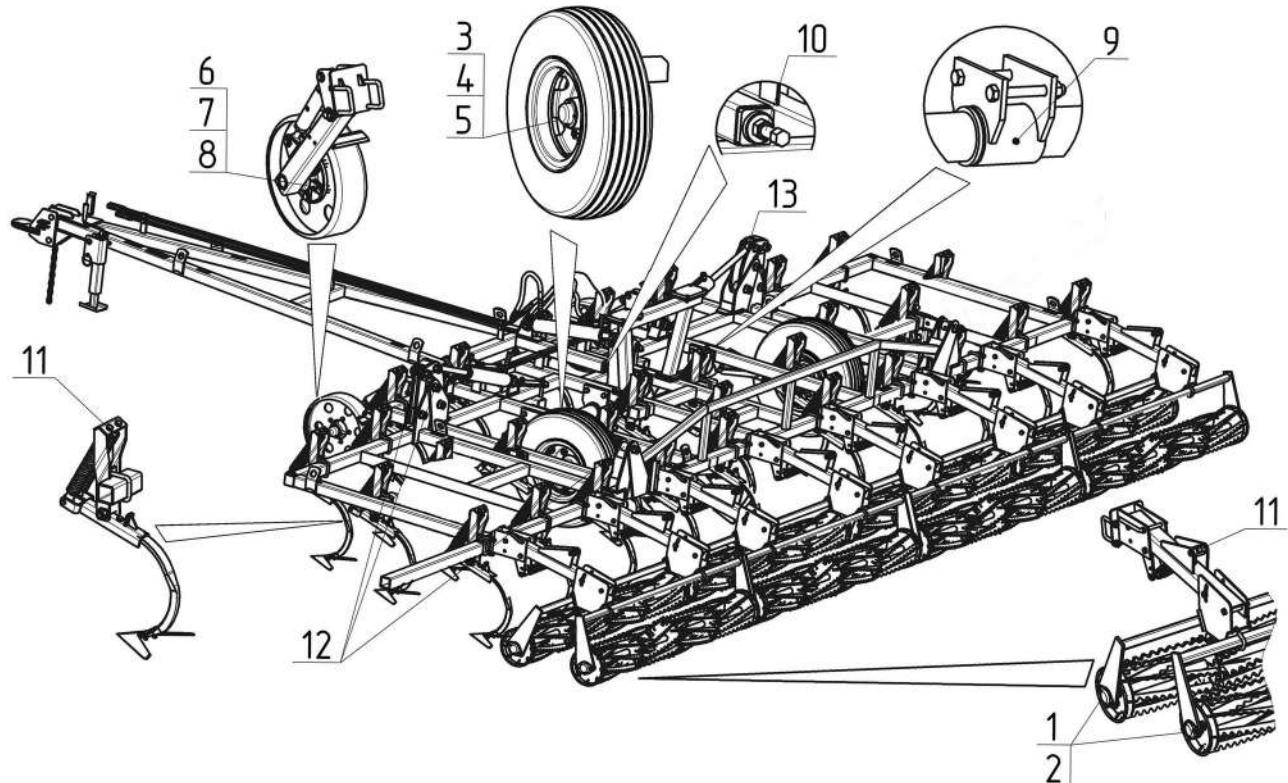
Места смазки. Схема расположения подшипников и манжет
